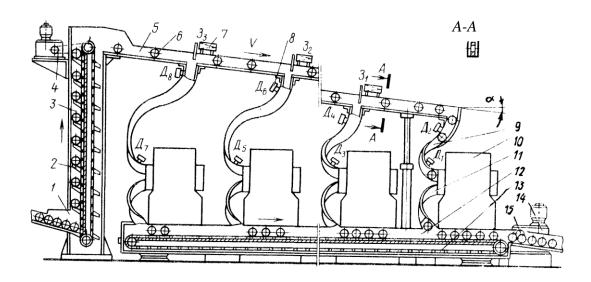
Схема транспортной системы токарного участка автоматического цеха № 2 (АЦ-2) 1-й ГПЗ: I — приемный лоток; 2 — захваты конвейераподъемника элеваторного типа; 3 — подъемник; 4 — привод конвейераподъемника; 5 — распределительный трассовый лоток; 6 — заготовки; 7 — заслонки; 8 — датчики переполнения подводящих лотков; 9 — подводящие лотки станков; 10 — станки; 11 — отводящие лотки станков; 12 — отводящий конвейер; 13 — ролико-втулочная цепь конвейера; 14 — привод отводящего транспортера; 15 — отводящий лоток к следующему участку
